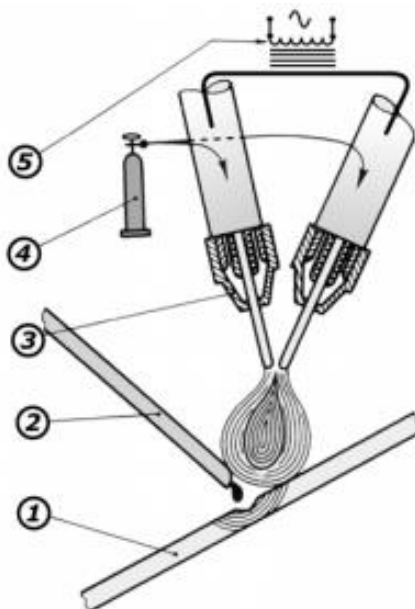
Soldadura atómica con atmosfera H_2
